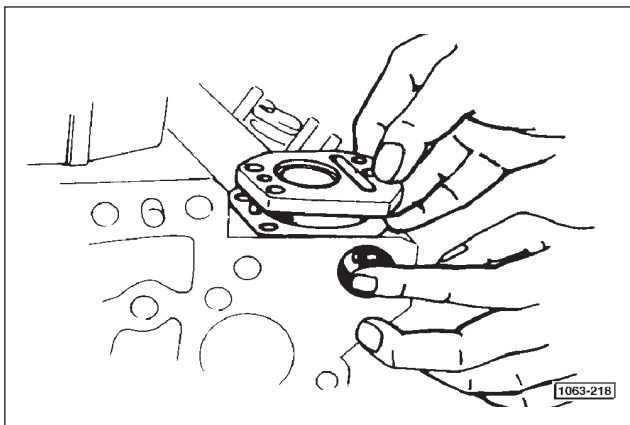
SEULEMENT POUR TRACTEURS EQUIPES DE RÉGULATEUR MECANIQUE - Placer le renvoi à équerre dans son logement sur le bloc en interposant les joints d'épaisseur permettant le réglage du jeu entre les dents des pignons (voir page 64).
